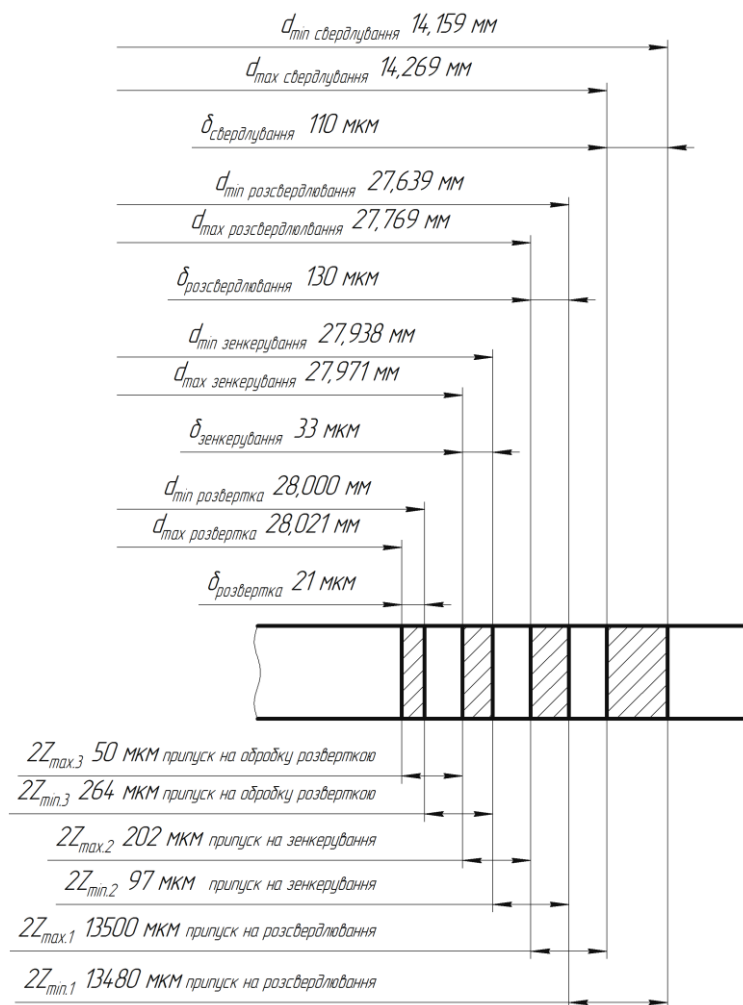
Схема розташування полів допусків і припусків
